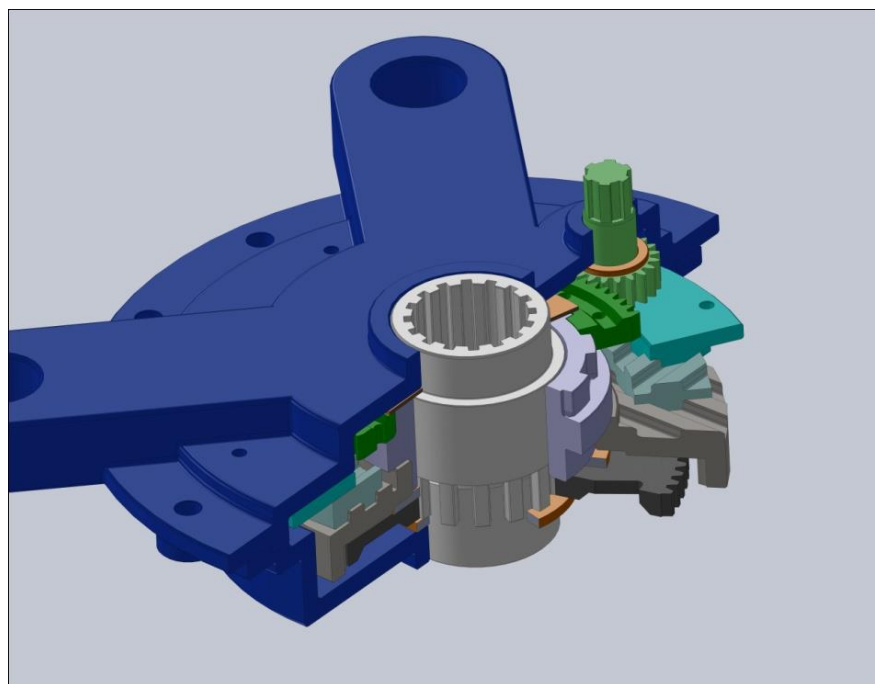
Внешний вид редуктора эксцентрикового типа «ЭР -150»
